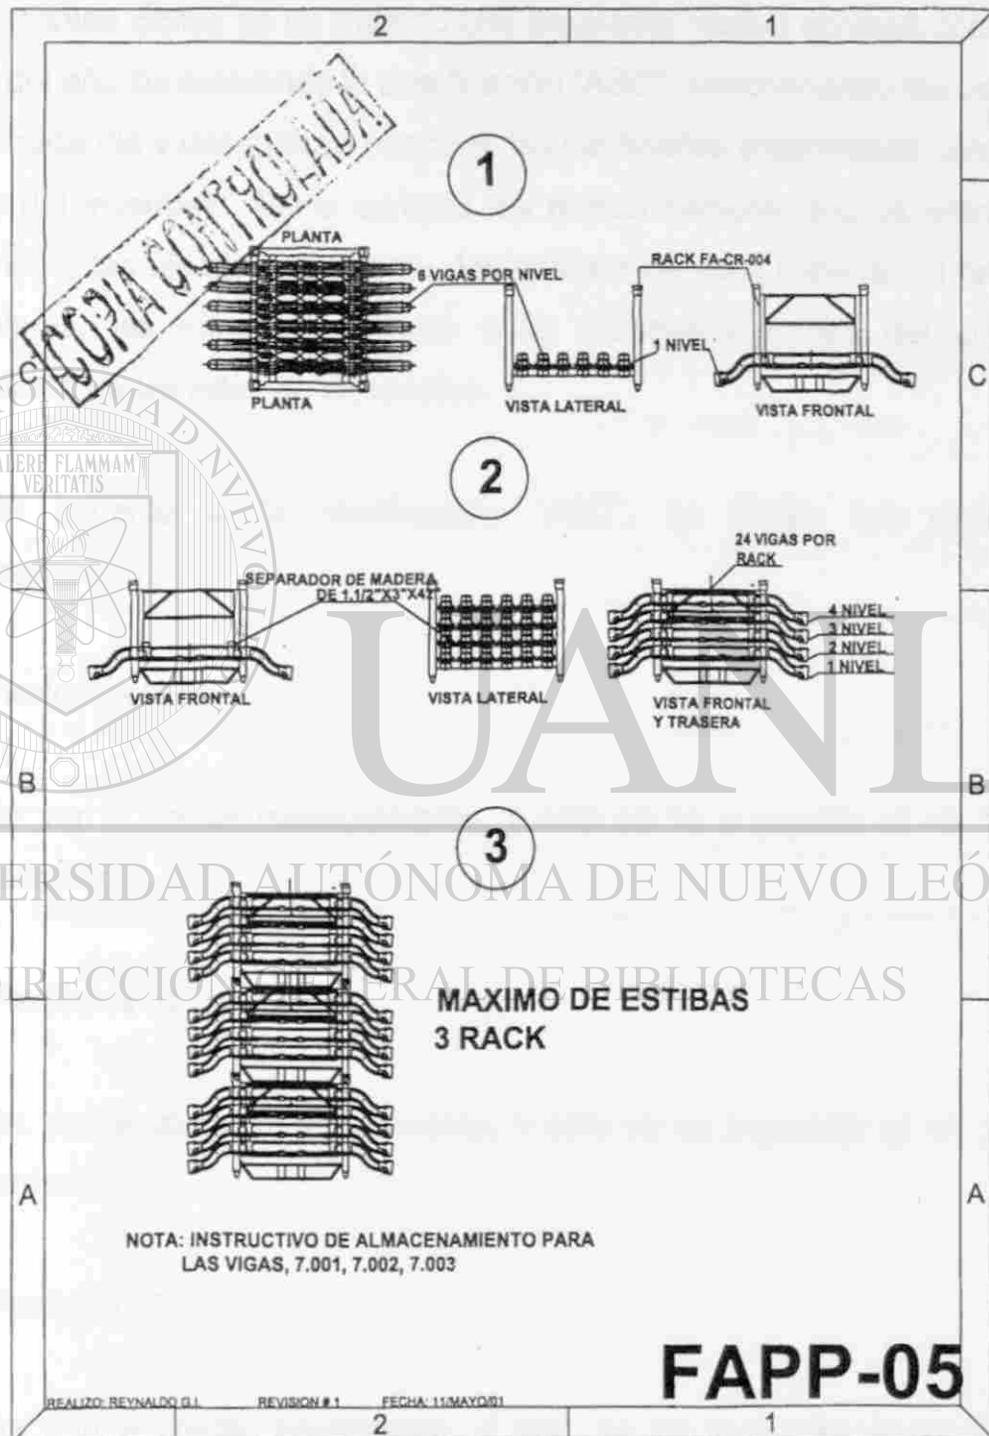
Instructivo para almacenamiento de viga 7.001 al 7.003.
